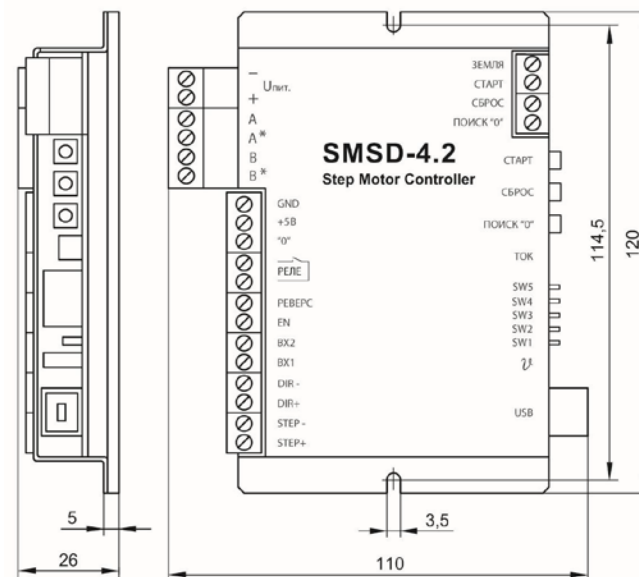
Габаритные размеры блока управления SMSD-4.2.
